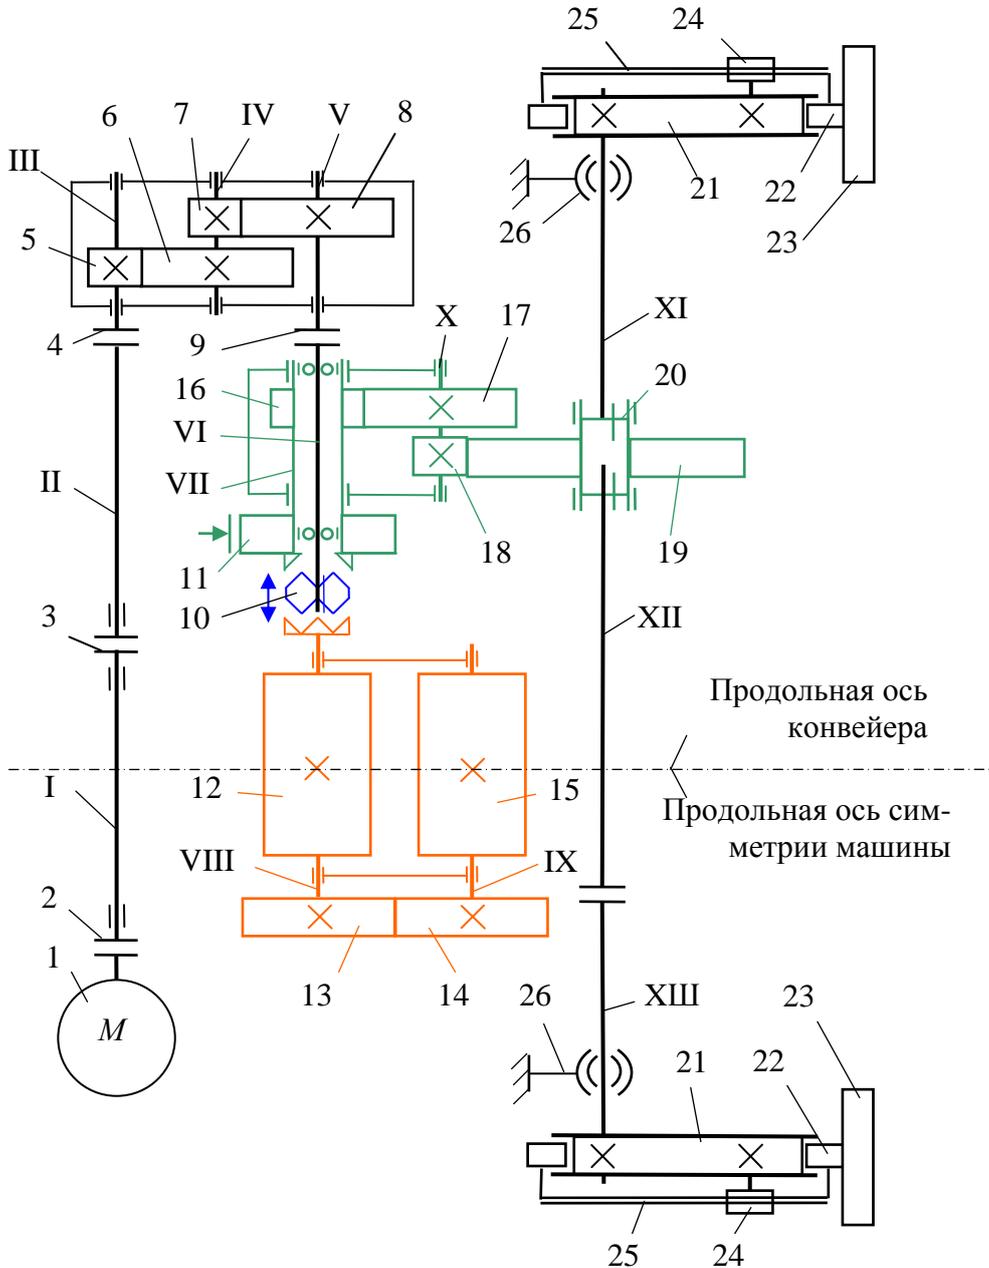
Кинематическая схема привода кулачков механизма шагания и барабанов ленточного конвейера
